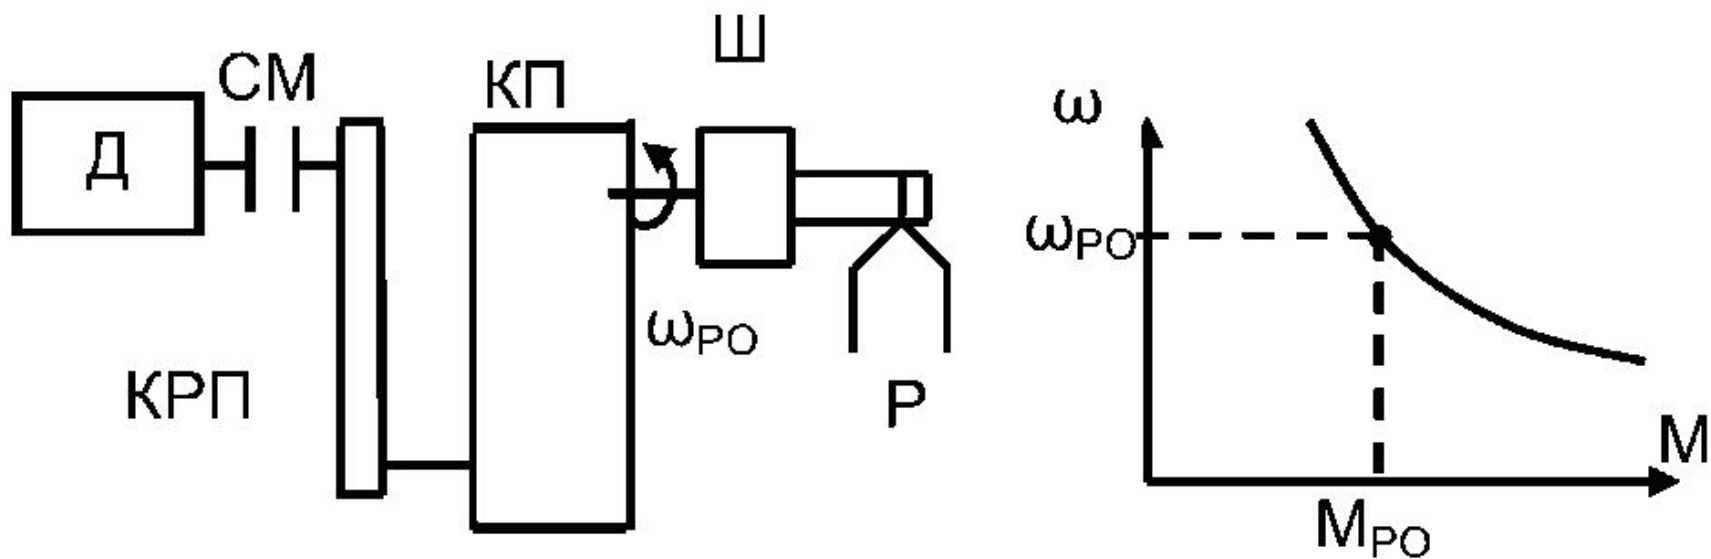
Кинематическая схема и механическая характеристика шпинделя токарного станка
